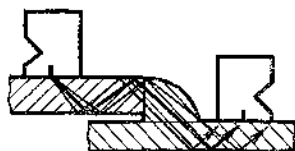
Контроль нахлесточных швов двумя излучателями
